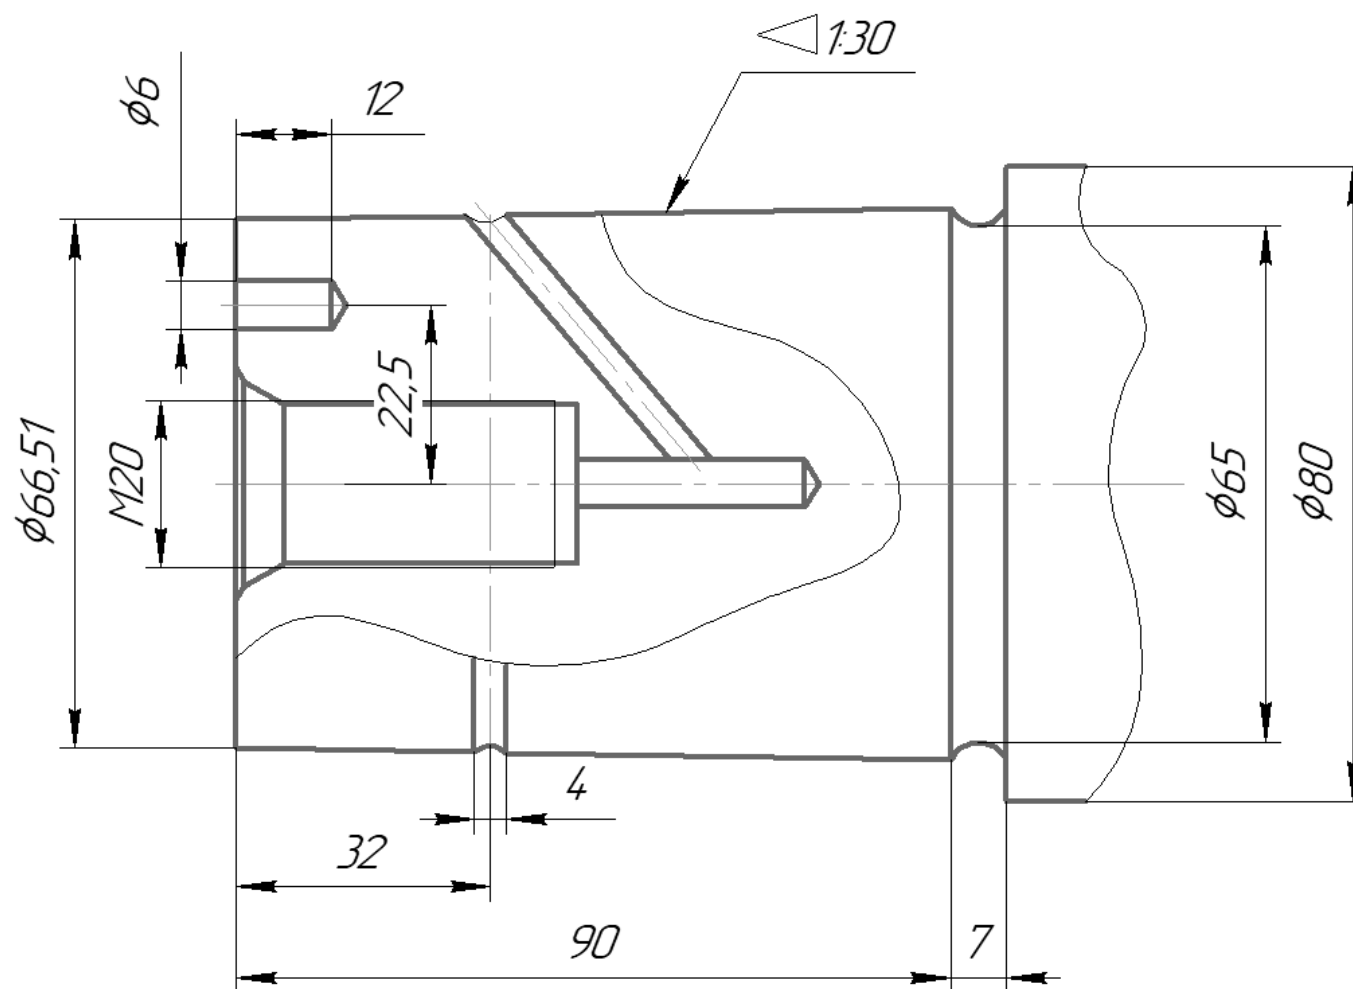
Присоединительные размеры приводного конца вала ТАД
